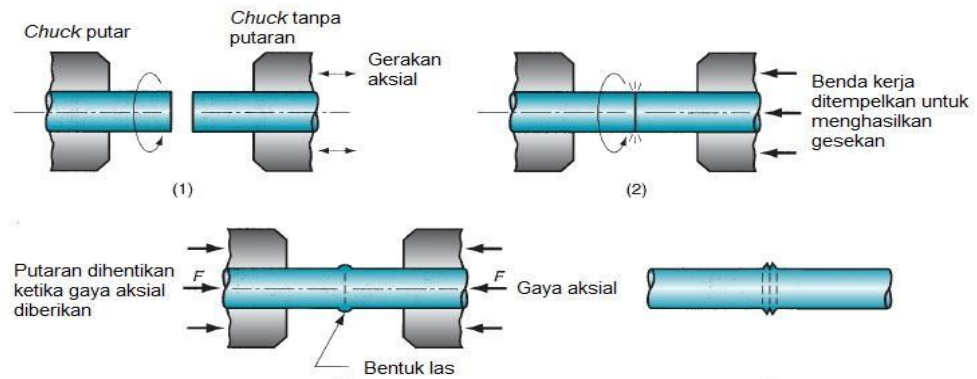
Friction Linier Welding* (Bhamji, 2010)
